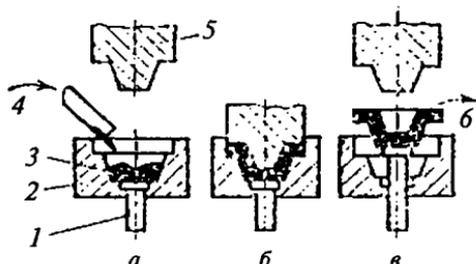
Схема и стадии процесса жидкой штамповки: 1 — выталкиватель; 2 — матрица; 3 — металл; 4 — желоб; 5 — пуансон; 6 — изделие
